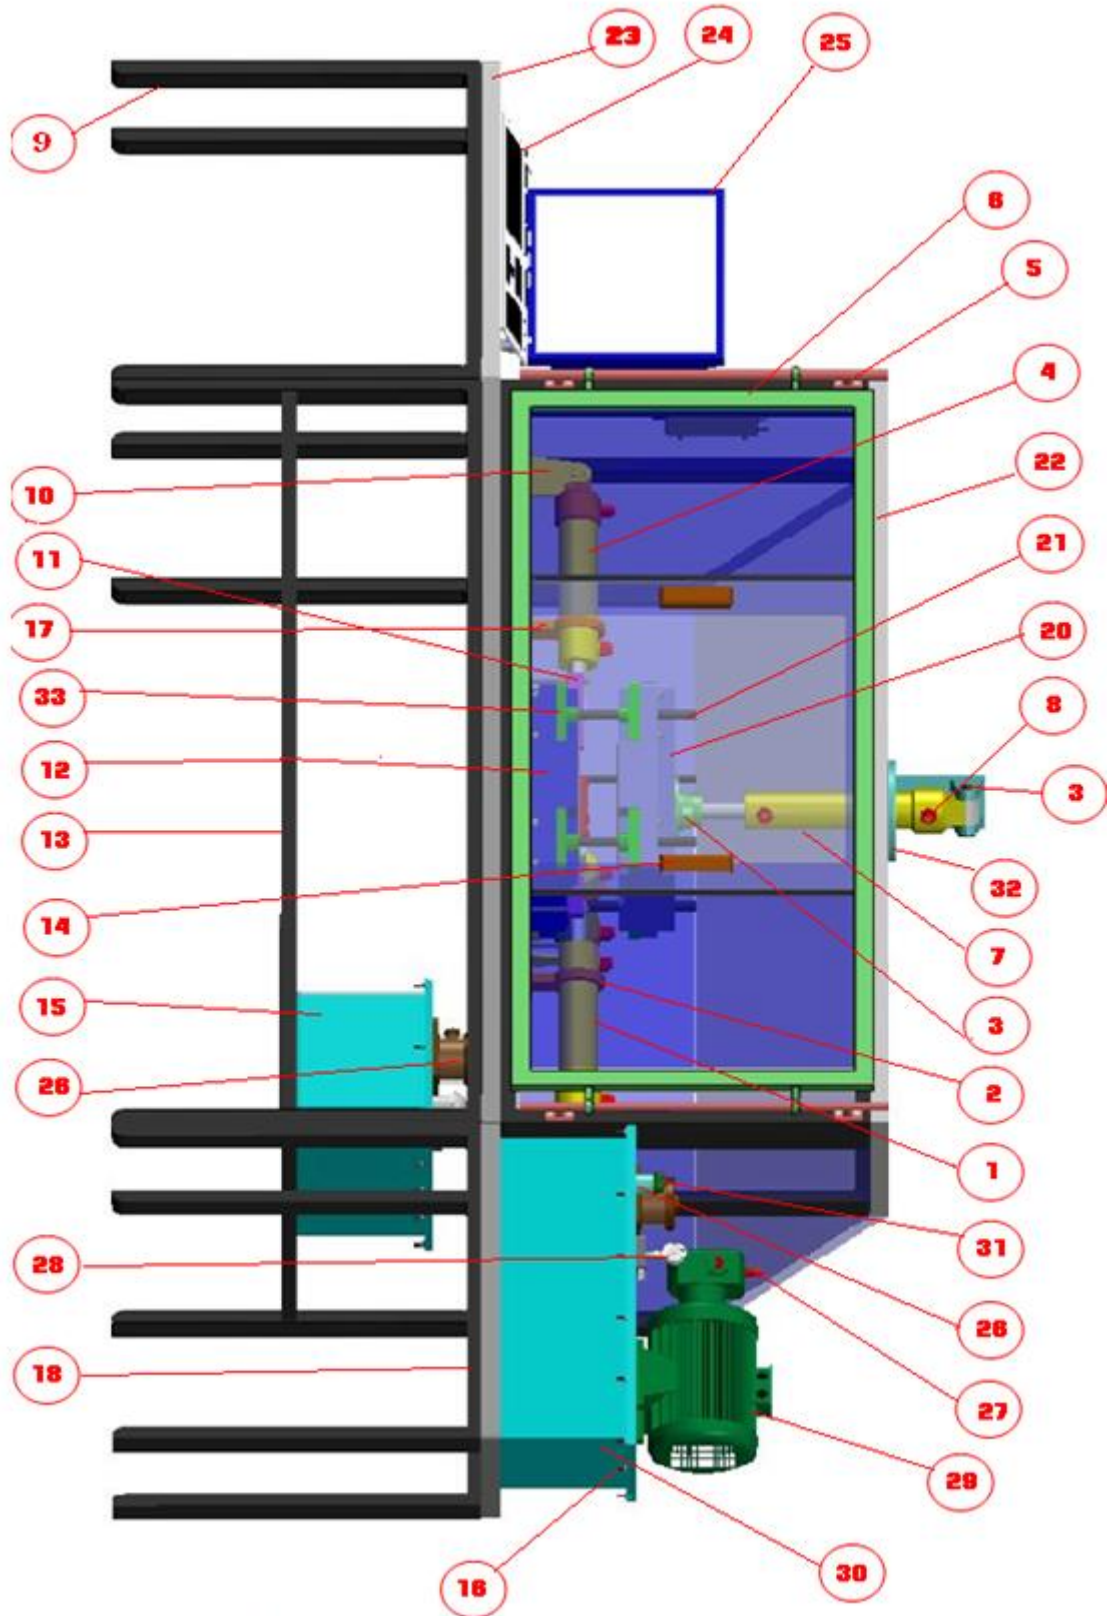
vue en perspective du dispositif hydraulique pour la fabrication de tube t par procédé hydroformage avec solide Works
